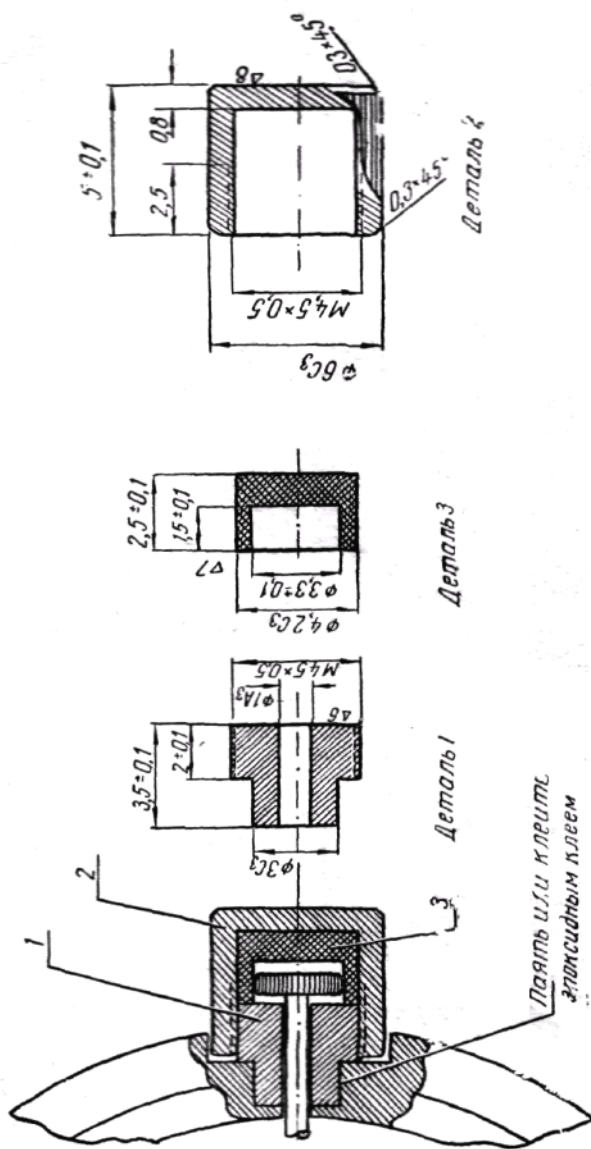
Рабочие чертежи: 1 — резбовая муфта; 2 — колпачок; 3 — герметизирующая прокладка
